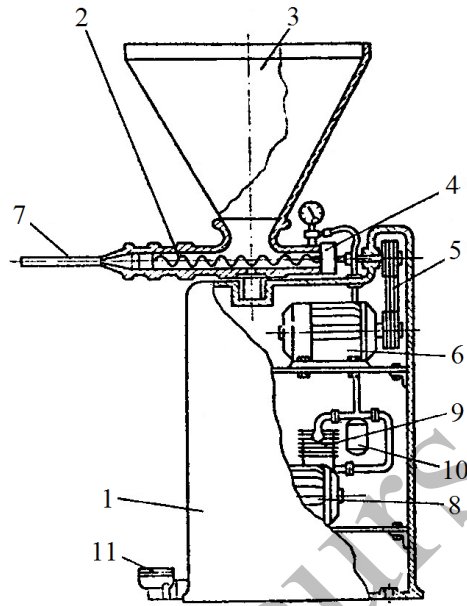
Schema mașinii de umplut cu un melc și instalație de vid: 1-cadru; 2- melc umplere; 3- gura de alimentare; 4- reductor; 5- roți de curea; 6- motor transmisie; 7- țeavă de umplere; 8- motor pompă vid; 9- pompă vid; 10- separator de lichid; 11- pedală acționare.
